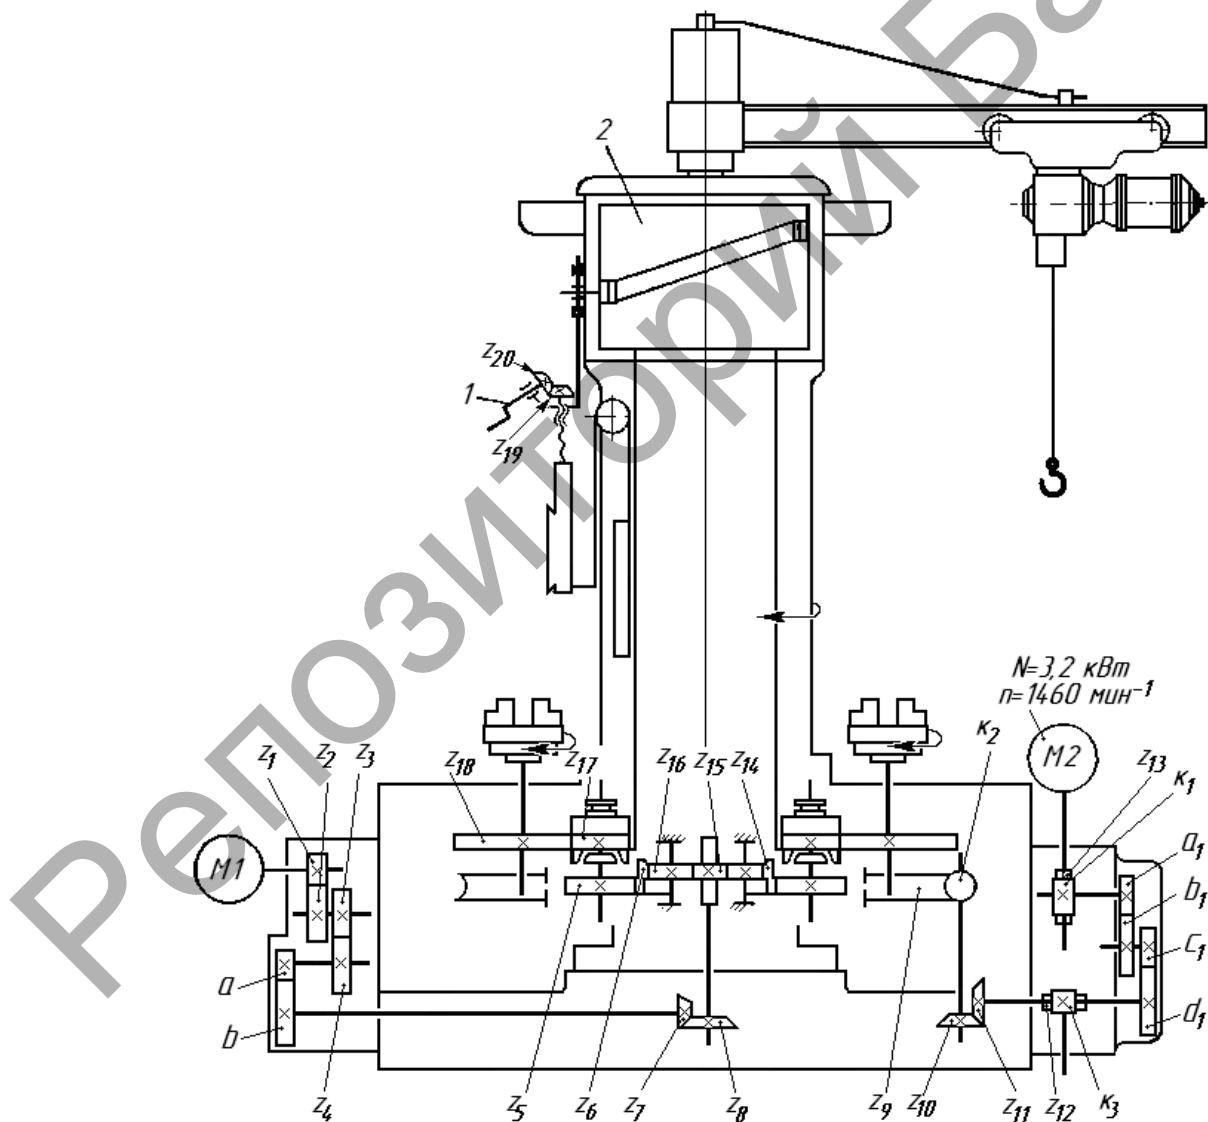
Кинематическая схема полуавтомата 1285
